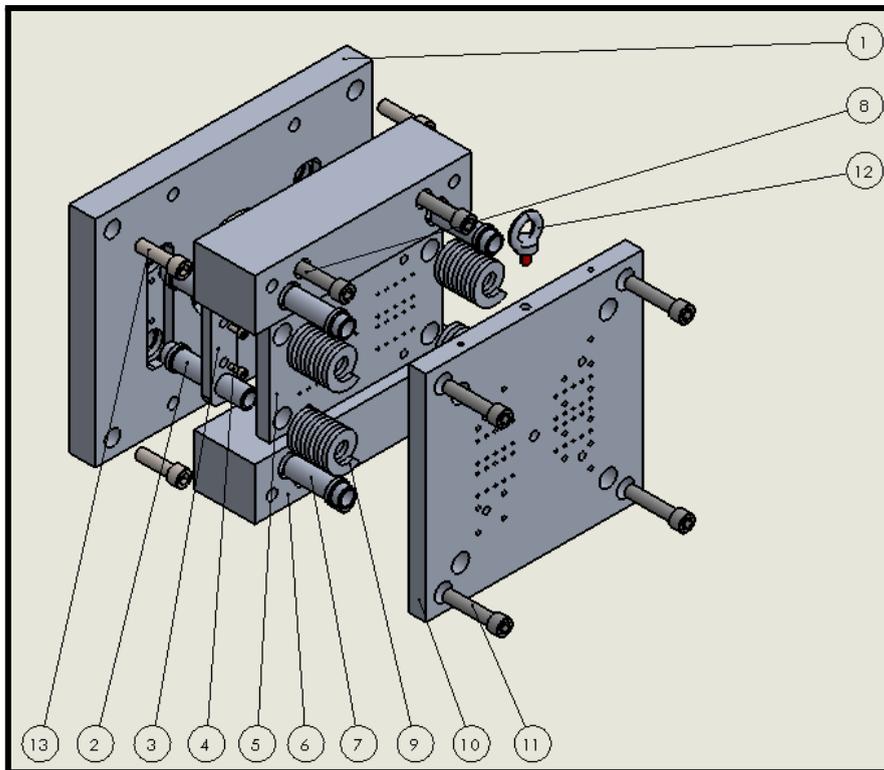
M. Vista explosionada de la configuración básica de la parte móvil del portamolde
